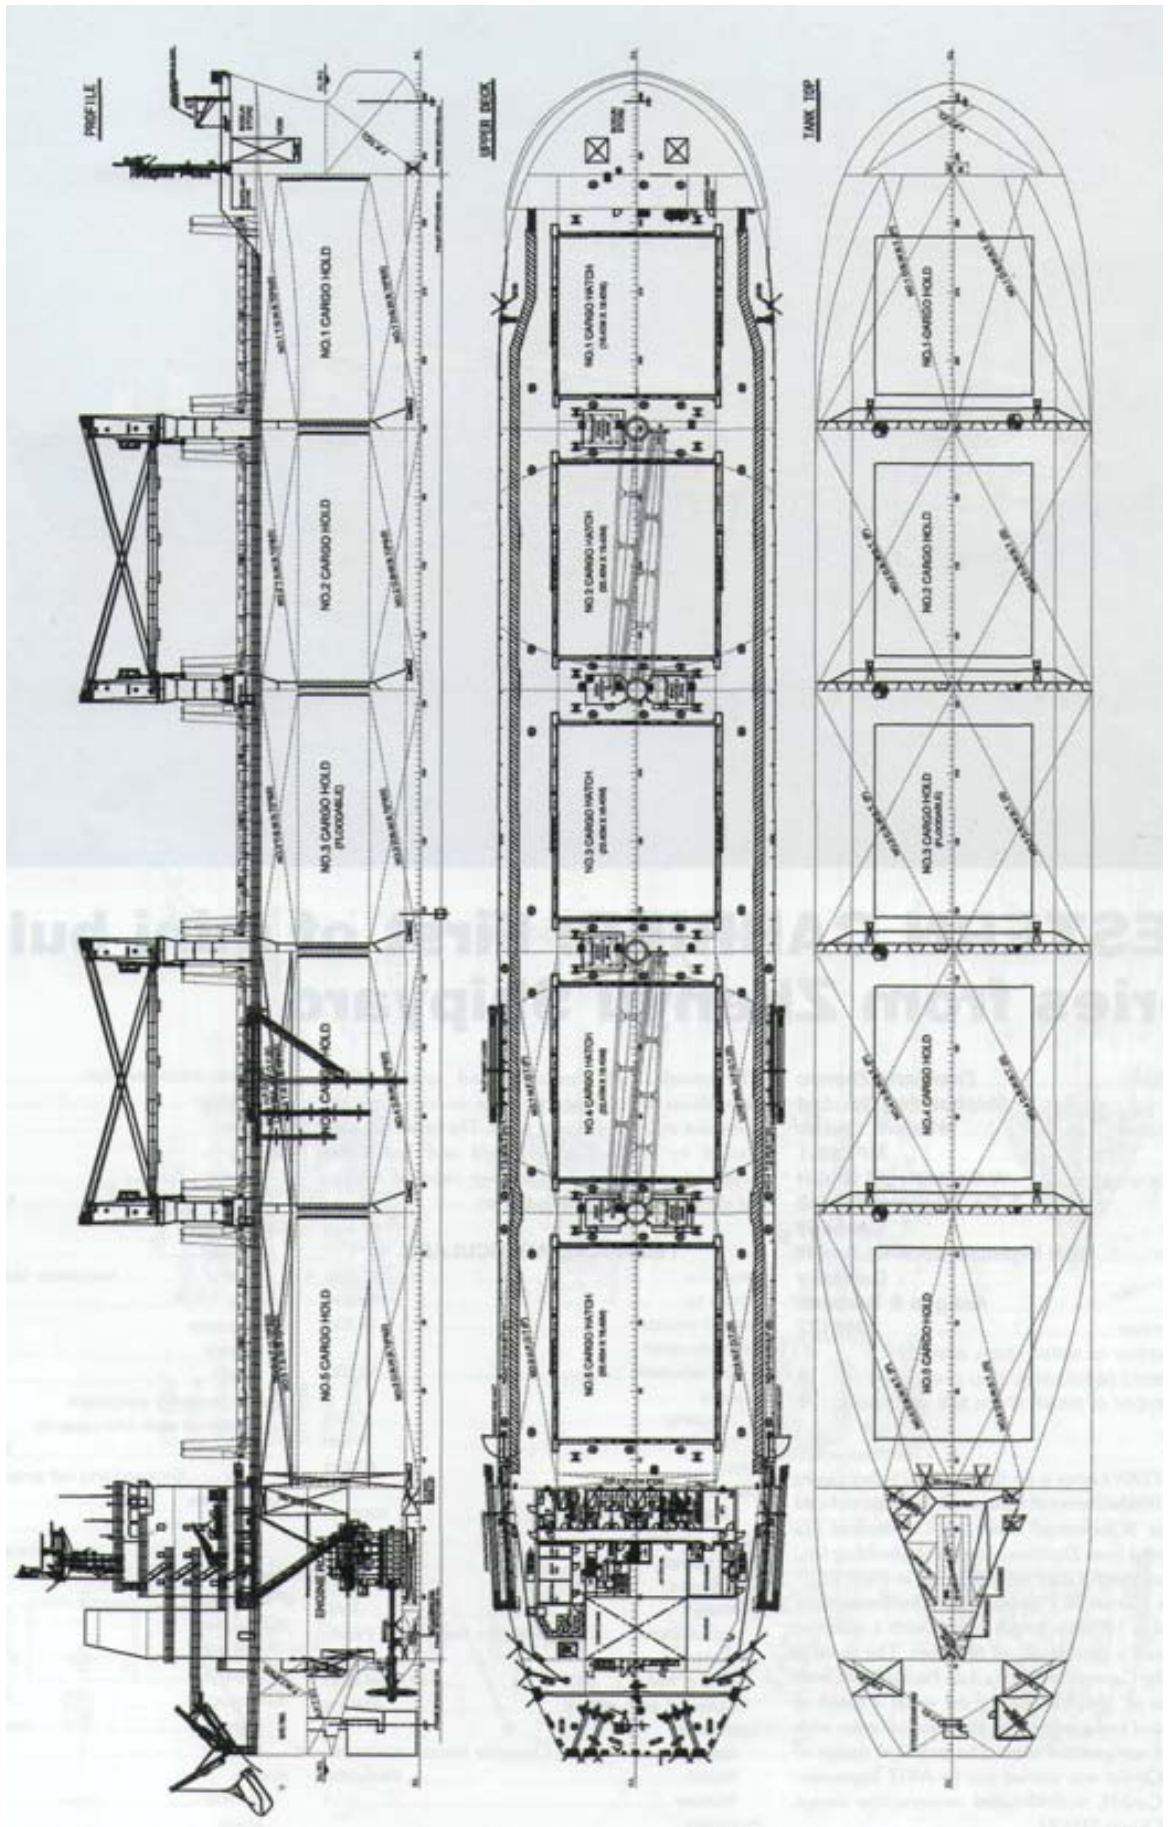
Загальний вигляд балкера Thalassini Axia
